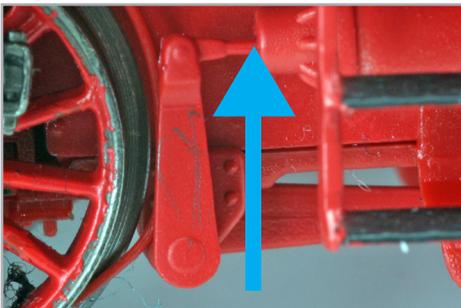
Umlenkhebel in Bremszylinder einführen
